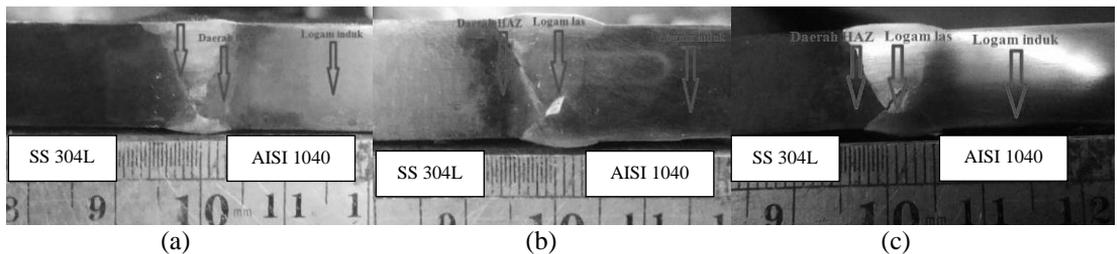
Hasil pengujian tarik spesimen *dissimilar welding* stainless steel 304L dengan baja karbon AISI 1040
